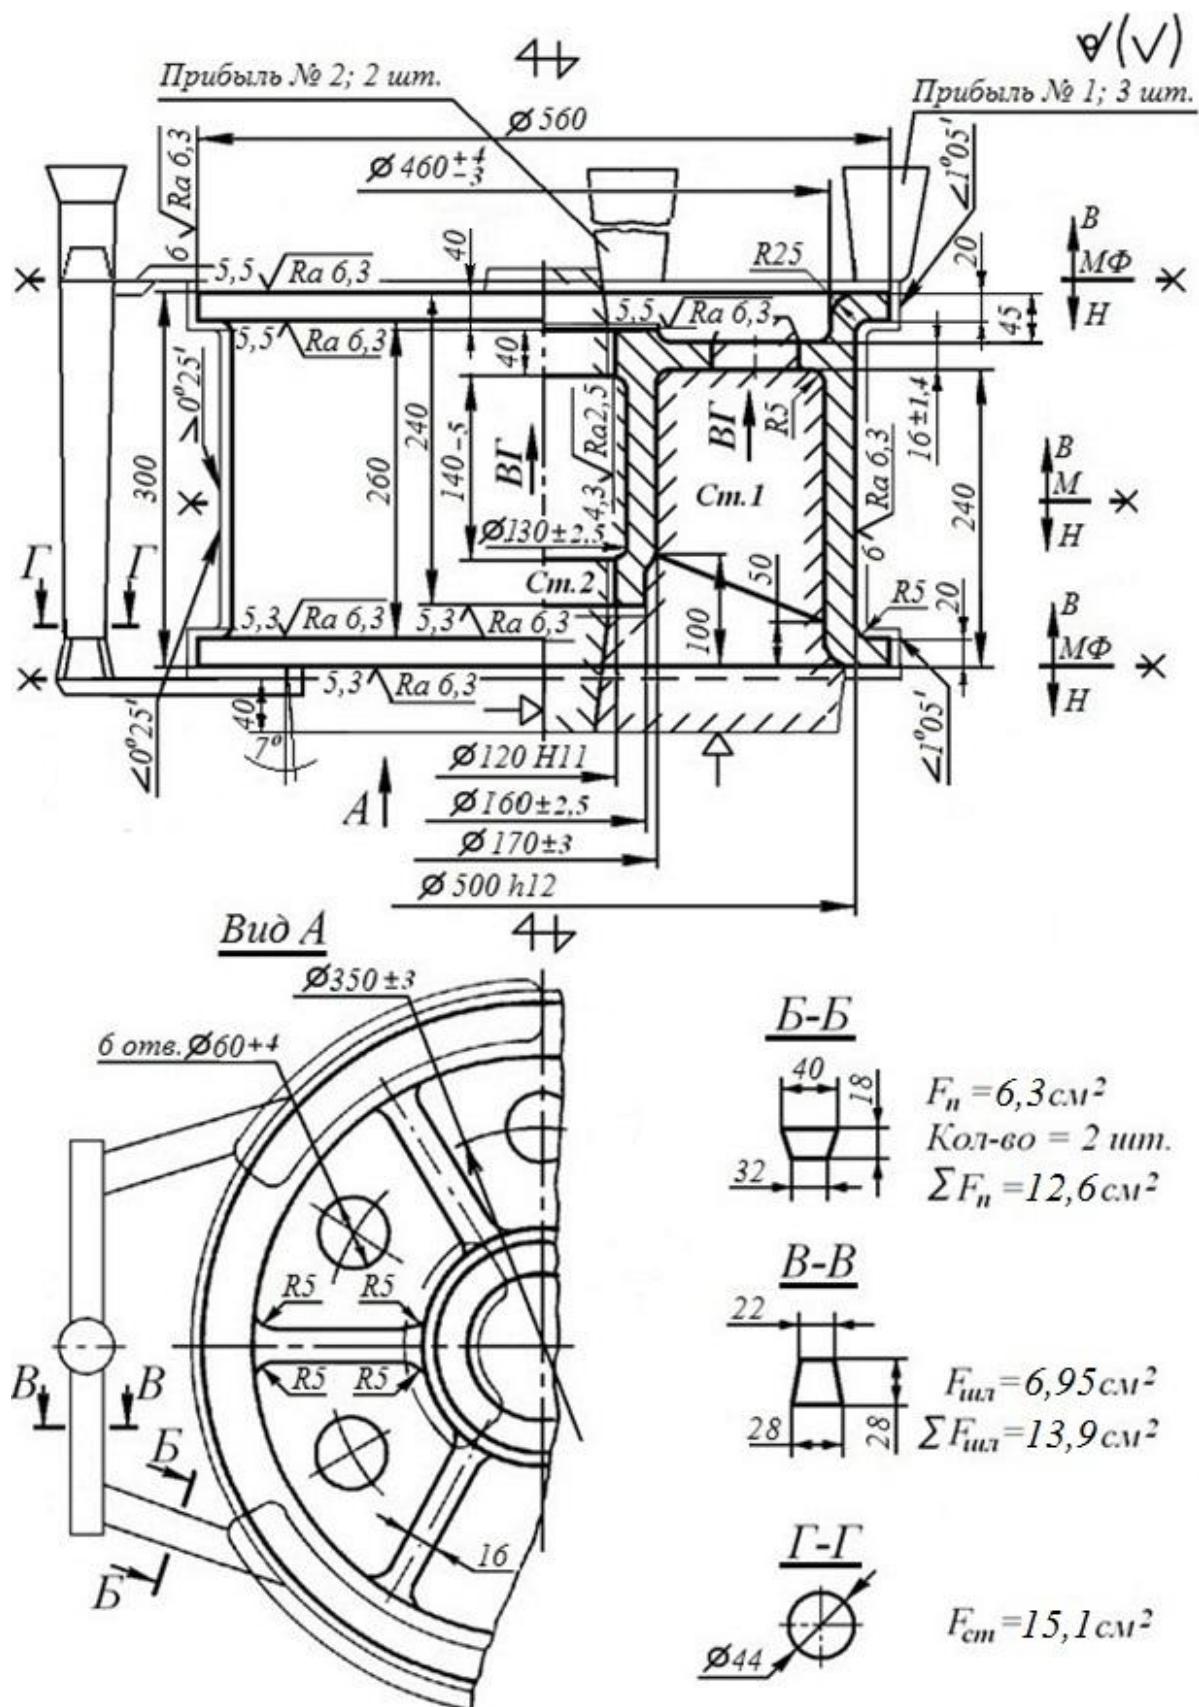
Чертеж детали «каток опорный» с элементами литейной формы
